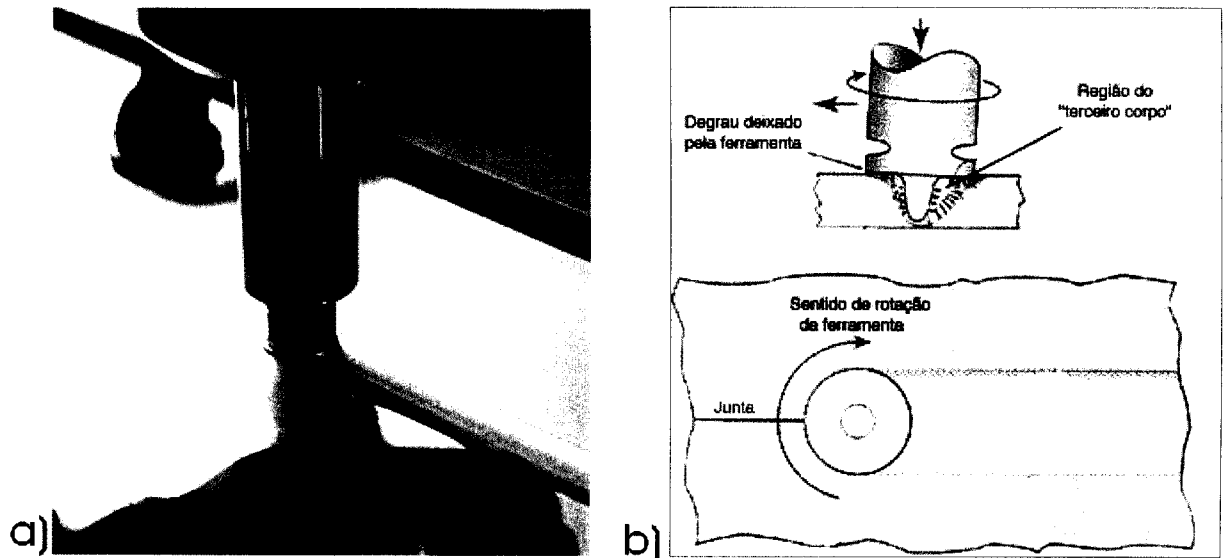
Processo de soldagem por FSW. (a) União de duas placas de alumínio por FSW, (b) desenho esquemático do processo apresentando a geometria da ferramenta.
